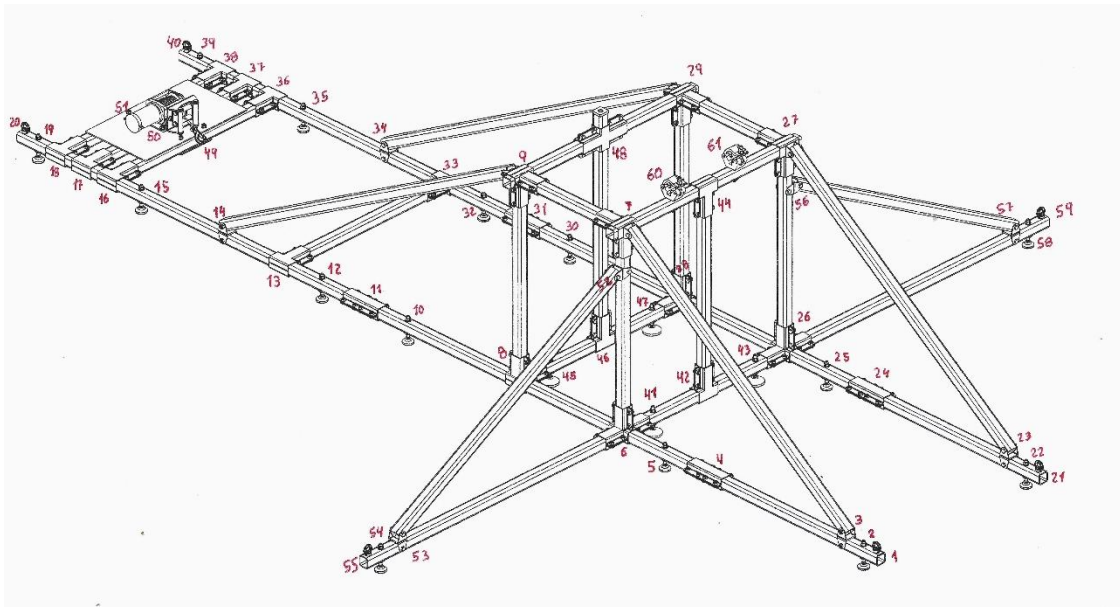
Conjunto pórtico de sujeción numerado por keyPoints.
